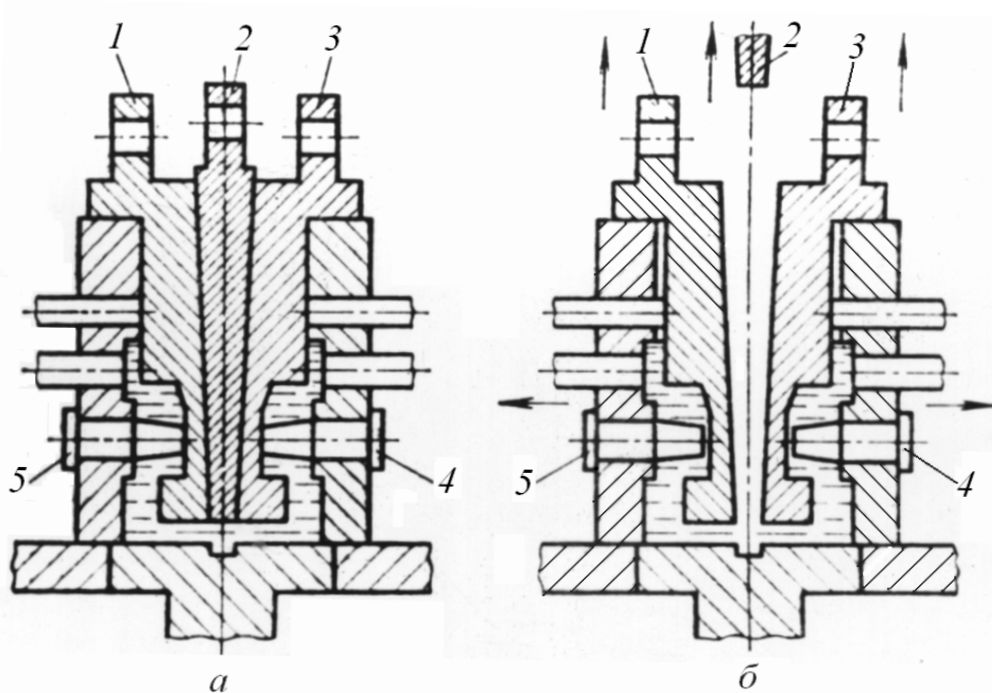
Кокіль для виливки поршня з рознімним металевим стержнем
